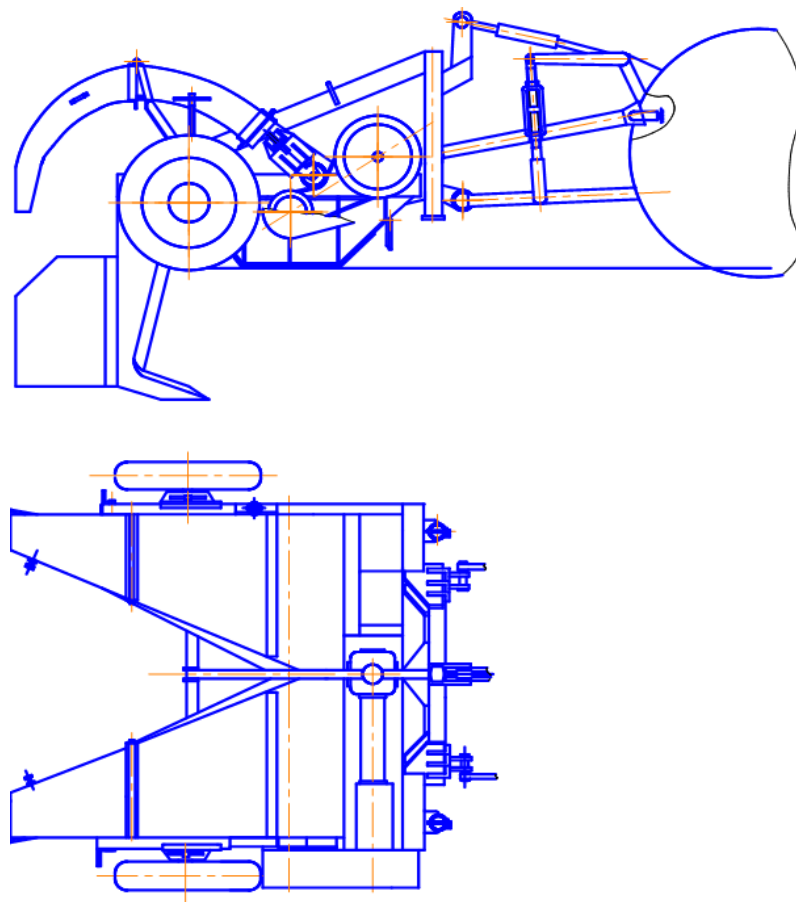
Конструктивна схема щілиноріза-наповнювача ЩЗН-1,5
